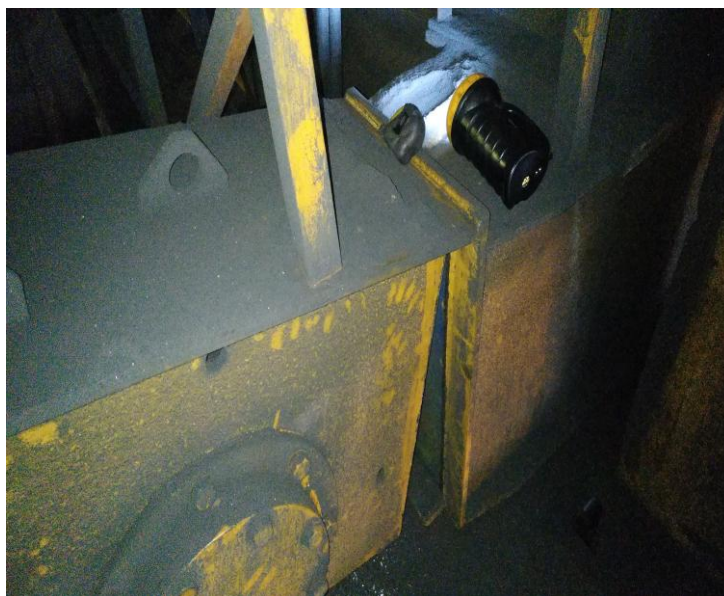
Разрушение сварных швов по границе металла сплавления соединения модуля холостого колеса с вертикальным листом концевой балки
